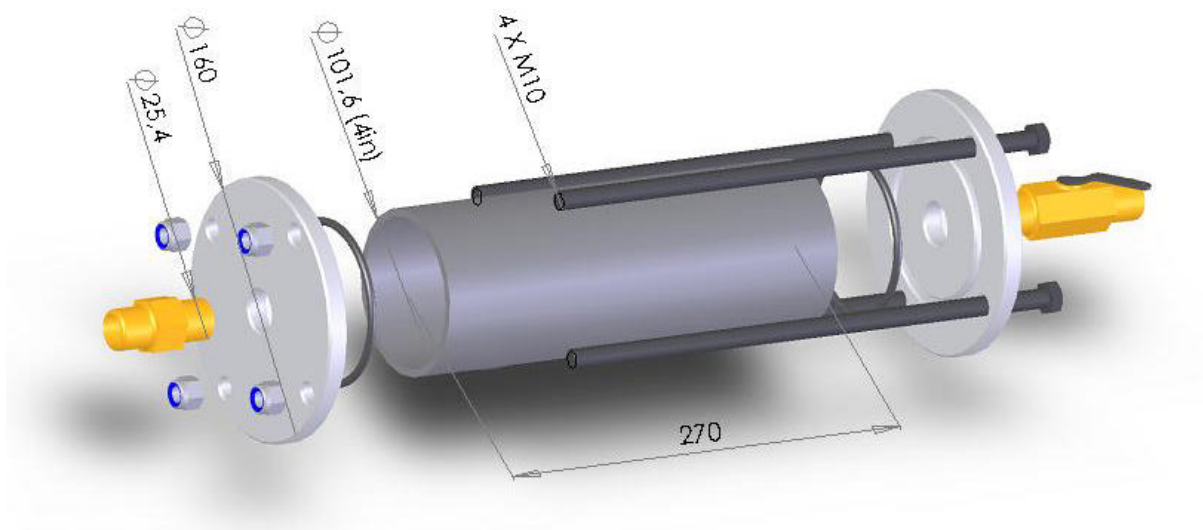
Vista em explosão do dispositivo de vedação do tubo
